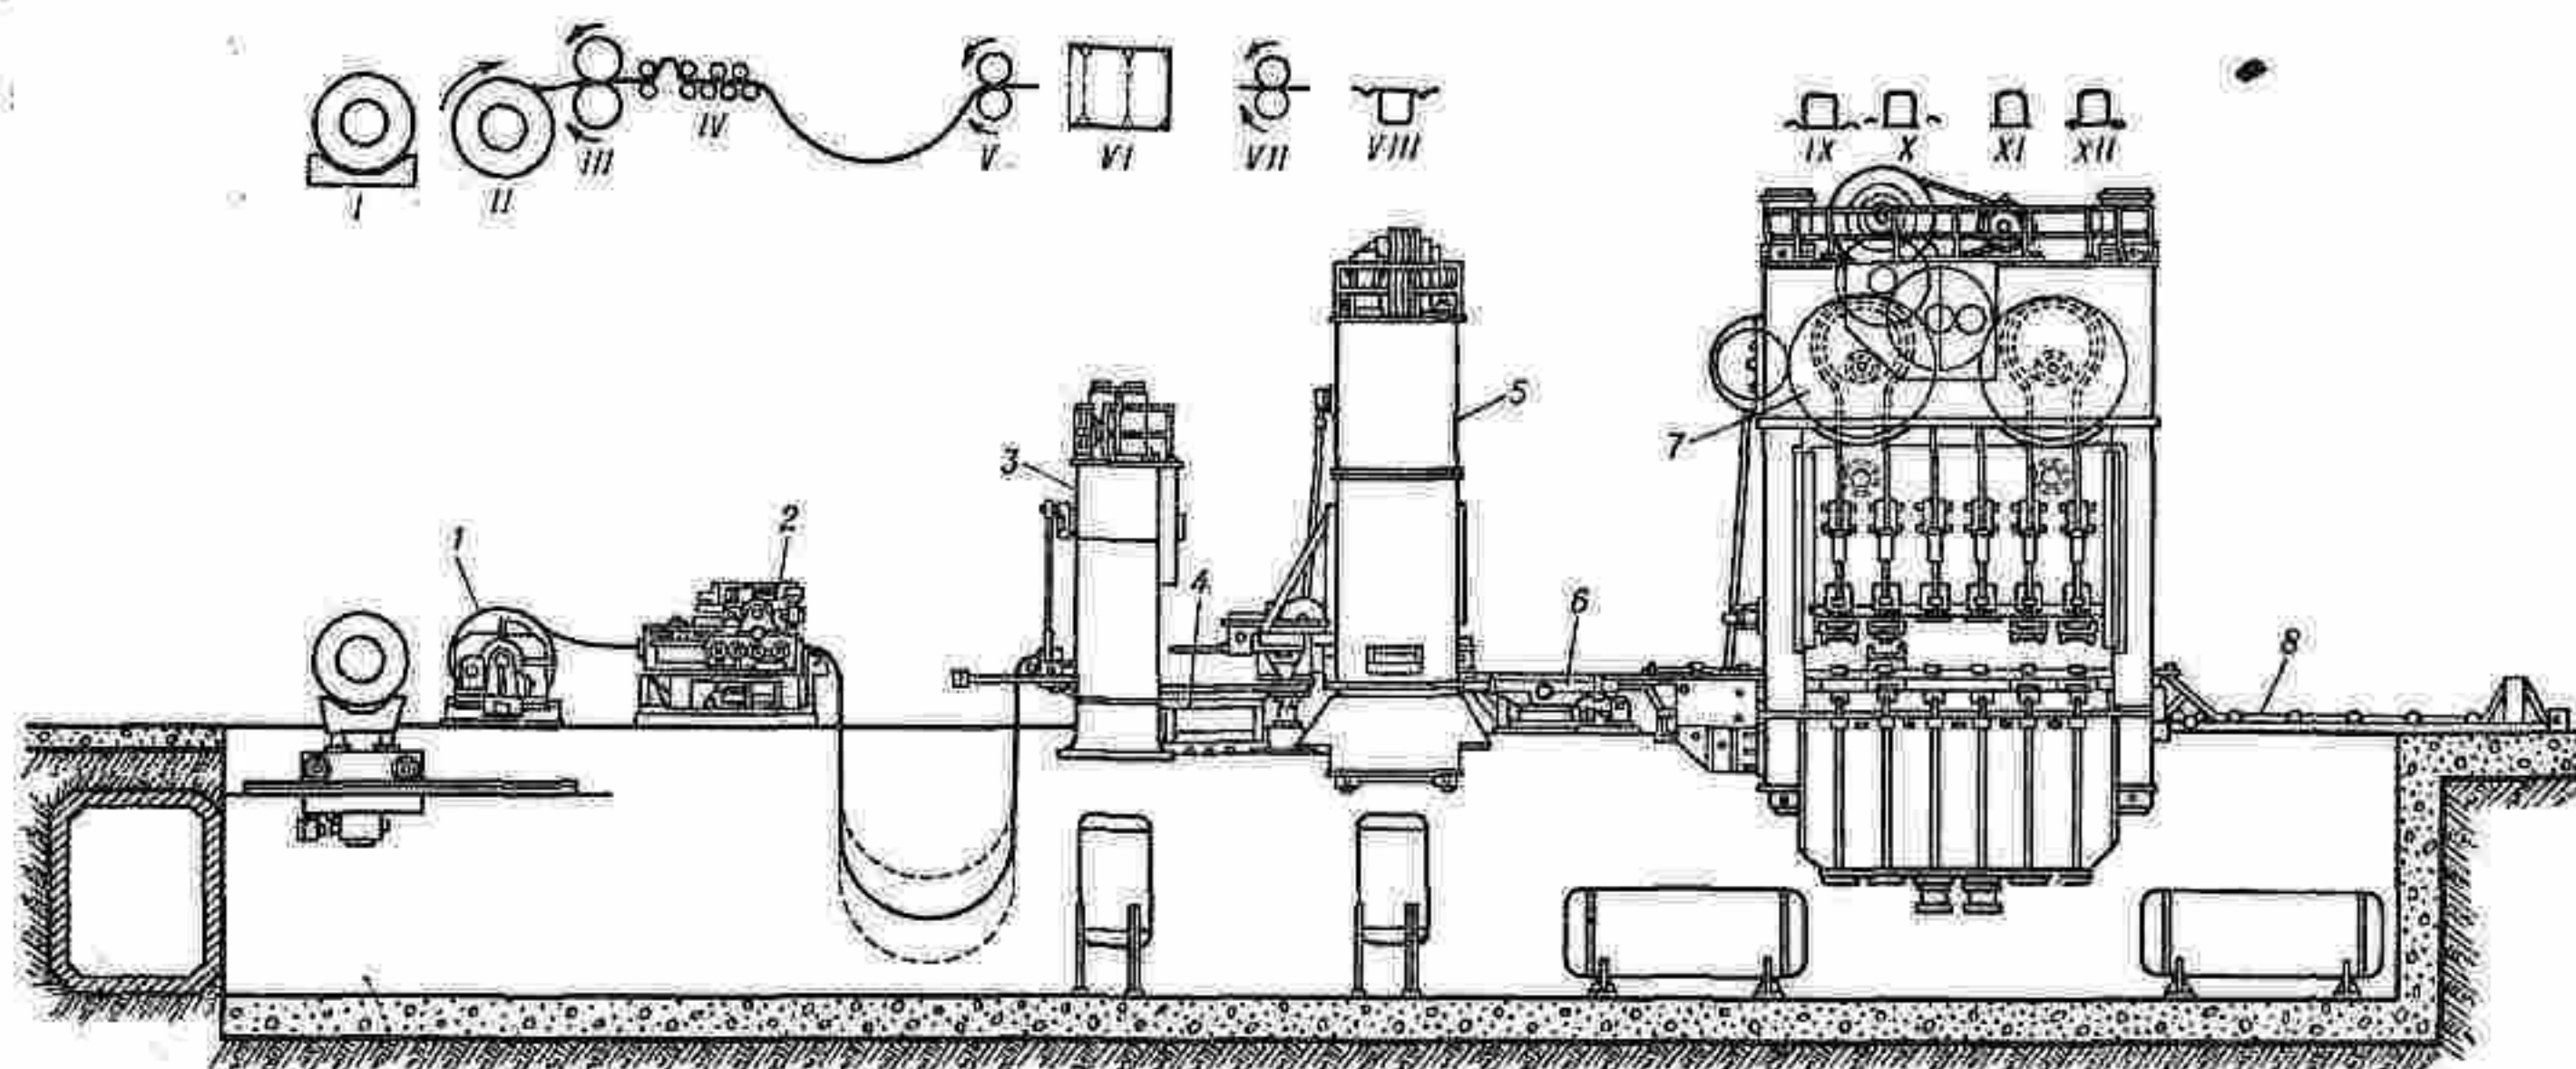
Схема автоматизированной линии для штамповки картеров двигателей: I — исходное положение рулона стальной ленты; II — размотка; III — чистка; IV — правка; V — подача; VI — вырубка заготовки; VII — смазка; VIII — вытяжка изделия; IX — переформовка радиусов и правка фланцев; X — обрезка фланцев по контуру; XI — формовка ребер жесткости и фланцовка по контуру; XII — пробивка отверстий; 1 — разматывающее устройство; 2 — листопрямляющая машина; 3 — двухкривошипный пресс простого действия с валковой подачей; 4 — механизм передачи и подъема стопы заготовок; 5 — однокривошипный пресс двойного действия для вытяжки; 6 — механизм передачи изделий и съема штампа; 7 — многопозиционный пресс с рейфферной подачей; 8 — механизм транспортирования изделий и съема штампа.
